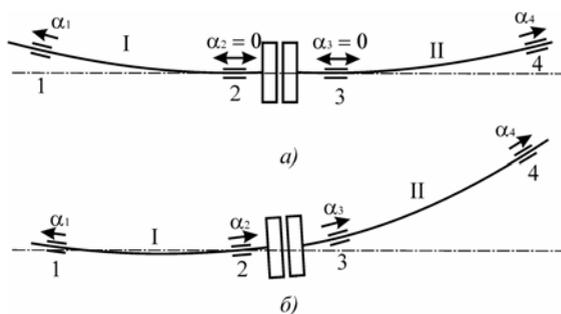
Различные способы установки линии валов двухмашинного агрегата
